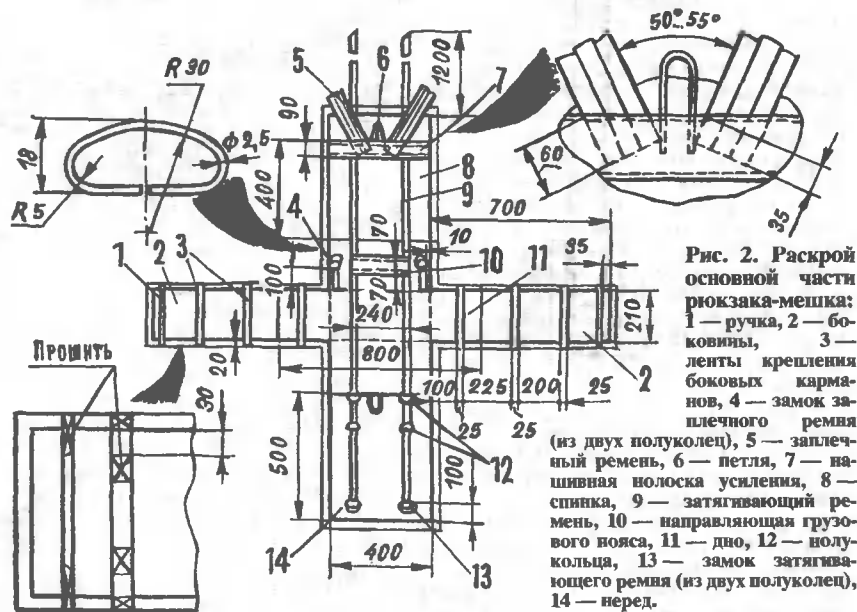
Раскрой основной части рюкзака-мешка: 1 — ручка, 2 — боковины, 3 — ленты крепления боковых карманов, 4 — замок заплетного ремня (из двух полуколец), 5 — заплетный ремень, 6 — петля, 7 — нашивная полоска усиления, 8 — спинка, 9 — затягивающий ремень, 10 — направляющая грузового пояса, 11 — дно, 12 — полукольца, 13 — замок затягивающего ремня (из двух полуколец), 14 — перед.
